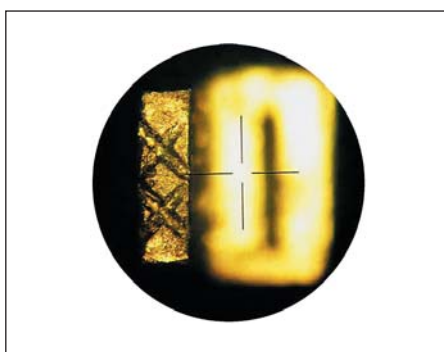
Внешний вид рабочего торца сварочного микроинструмента
